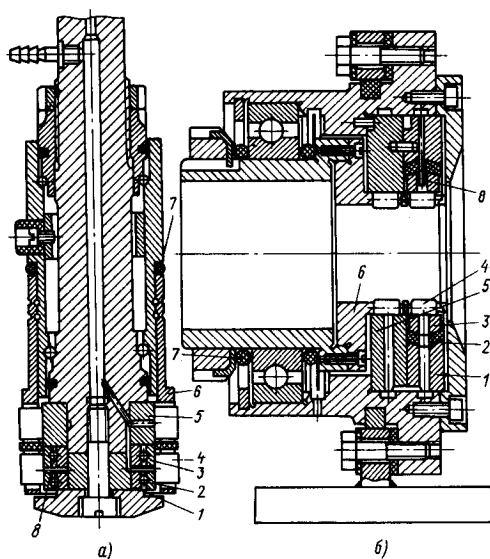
Двухрядный инструмент ударного действия для обработки: а — отверстий; б — наружных цилиндрических поверхностей; 1 — корпус упругой оправки; 2 — упругий элемент (резиновое кольцо); 3 — рабочее кольцо; 4 — ролики; 5 — жесткая оправка; 6 — сепаратор; 7 — упругое кольцо; 8 — штифт
